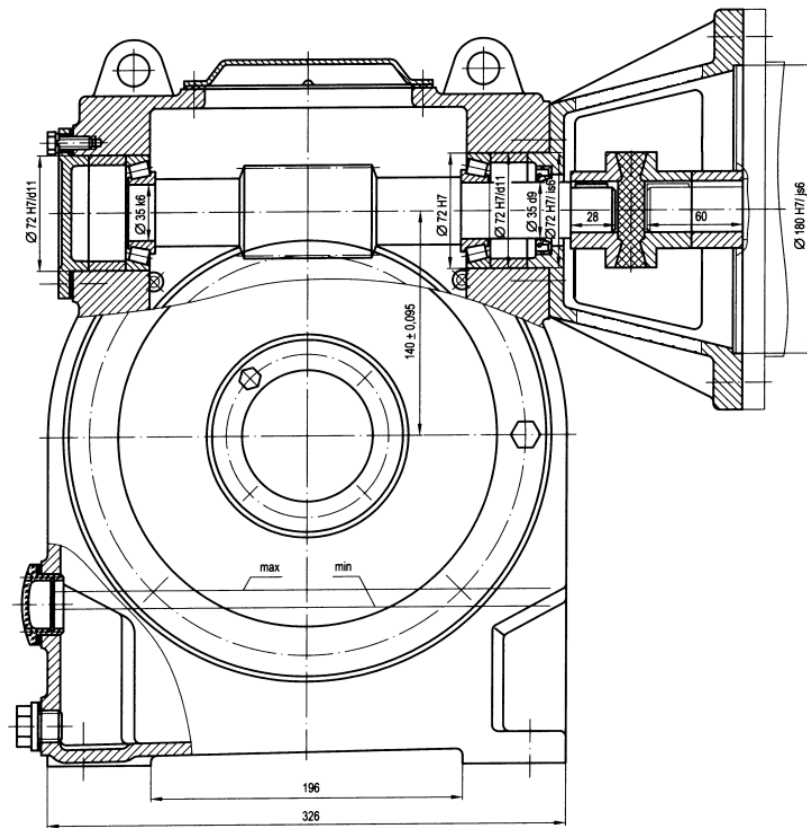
Редуктор с верхним расположением червяка и конусом для крепления фланцевого двигателя
